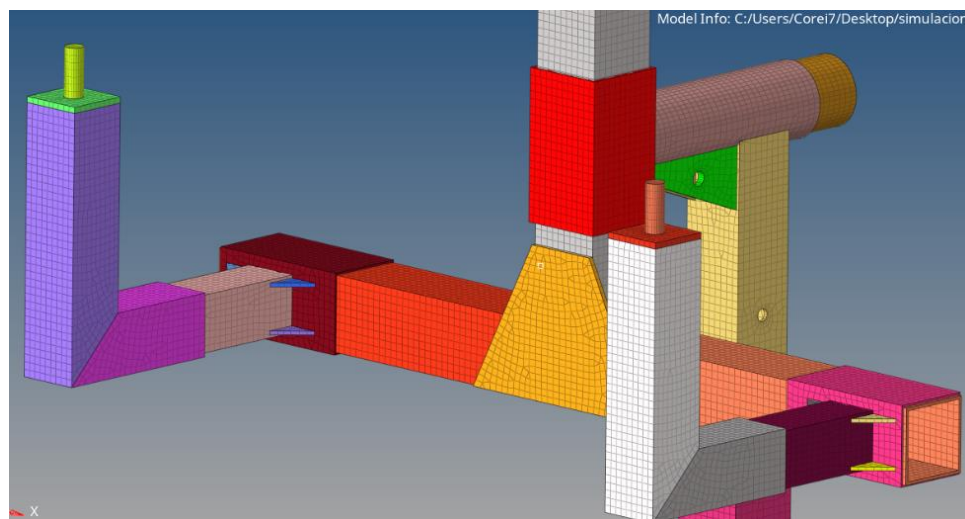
Mallado 2D en el ensamblaje estructural del equipo
